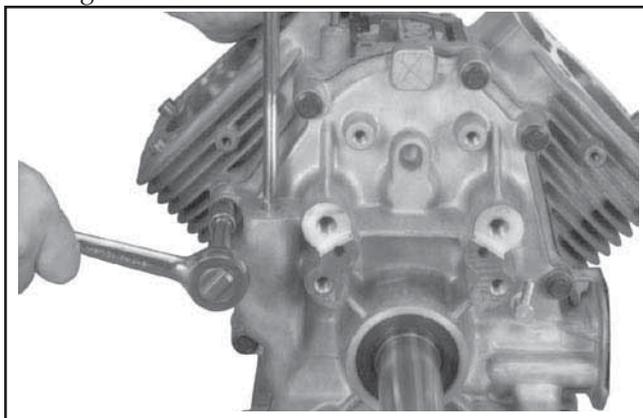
Enlèvement des dix raccords de la plaque de fermeture.
